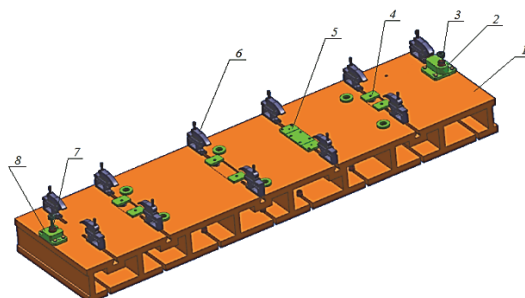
Электронный макет станочного приспособления для обработки детали «шассийная балка»
